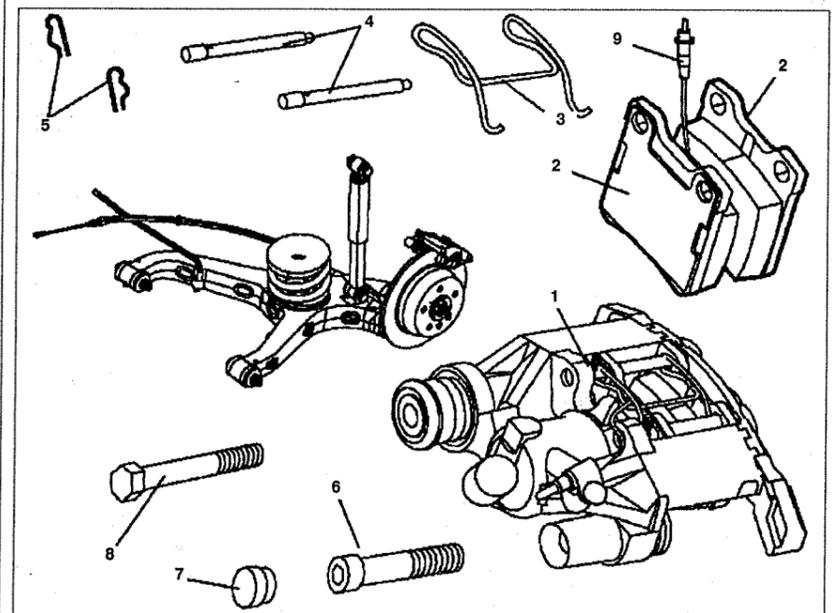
Тормозные колодки заднего тормозного механизма:
